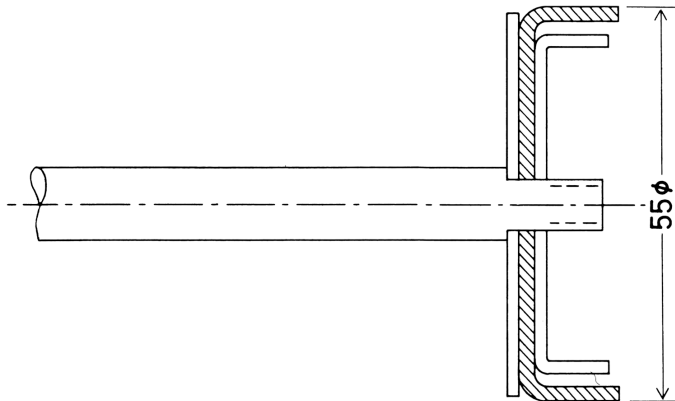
Kolben an Stange ohne Befestigungsmutter. Der schraffierte Teil ist aus Leder. Sobald im Innern des Zylinders ein Unterdruck entsteht, hört die Wirkung der Dichtung auf und Luft kann ins Innere fließen. Bei Überdruck im Innern dichtet die an der Zylinderfläche anliegende Fläche ab.
